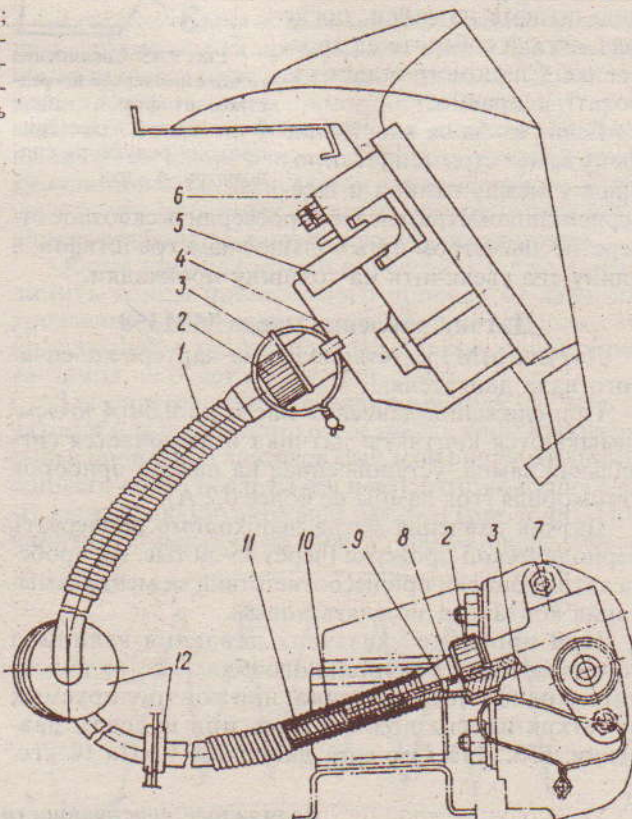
Гибкий вал спидометра и его привод: 1 - гибкий вал; 2 - гайка накидная; 3 - шплинт-проволока; 4 - спидометр; 5 - пружинная защелка комбинации приборов; 6 - комбинация приборов; 7 - редуктор привода спидометра; 8 - трос; 9 - шайба запорная; 10 - защитная трубка; 11 - оболочка; 12 - втулки уплотнительные
